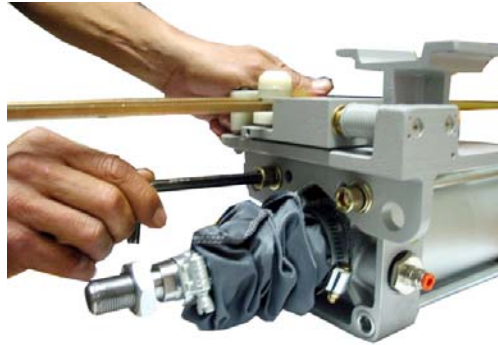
Desmontagem do Suporte do Posicionador FY301
